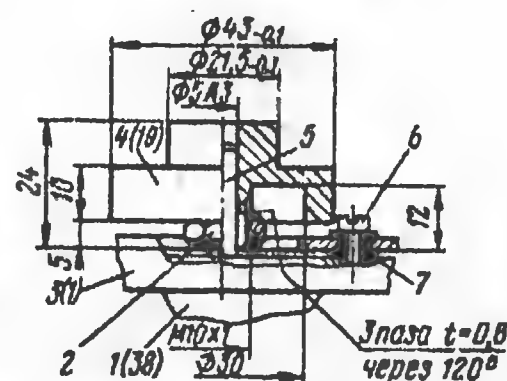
Узел ведущего двигателя: 1(38) — электродвигатель КД-3,5, закрепить на дет. 3(1) винтами 6 через втулки 7; 2 — гайка специальная (от поромонного резистора СП-11 или СП-111 со стопором оси); 3(1) — шасси узла ведущего вала; 4(19) — насадка с цапгой, Д16-Т, закрепить на дет. 5 гайкой 2; 5 — вал двигателя; 6 — винт М4×8, 3 шт.; 7 — втулка, резина, 3 шт.
